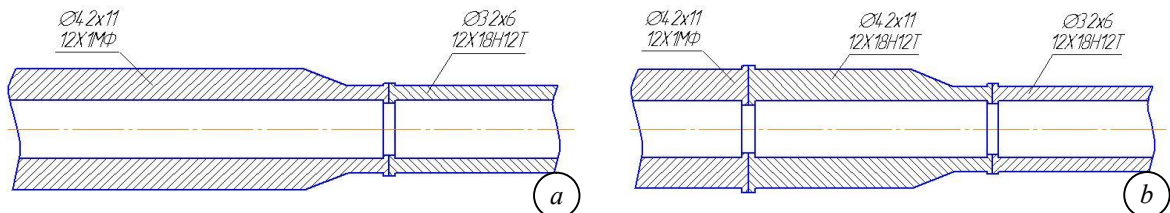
Зварне з'єднання різнорідних сталей: а – початкова конструкція; б – оновлена конструкція.
